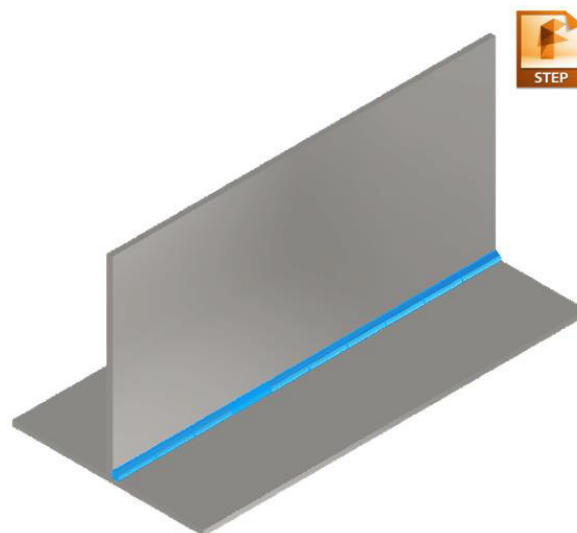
Geometría de junta T y cordón de soldadura obtenido.
